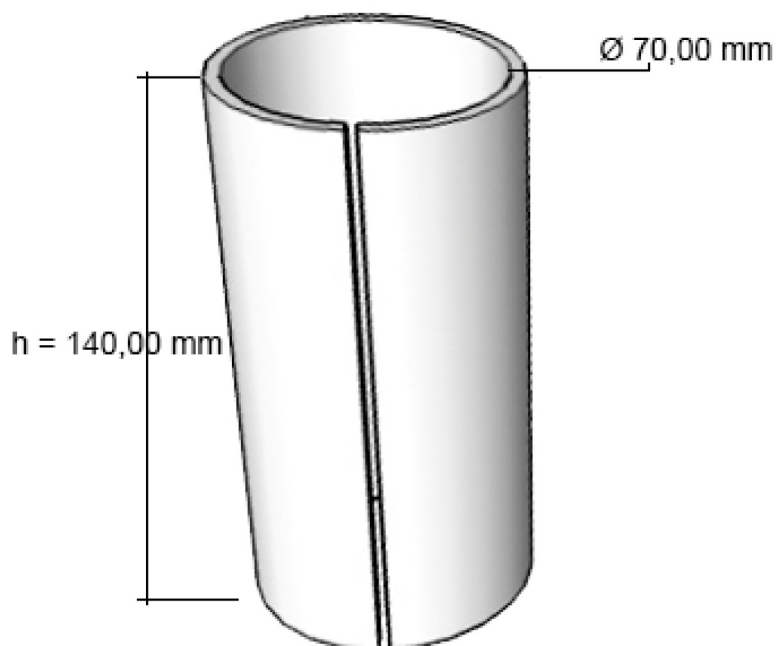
Molde para confecção de corpos de prova cilíndricos.
